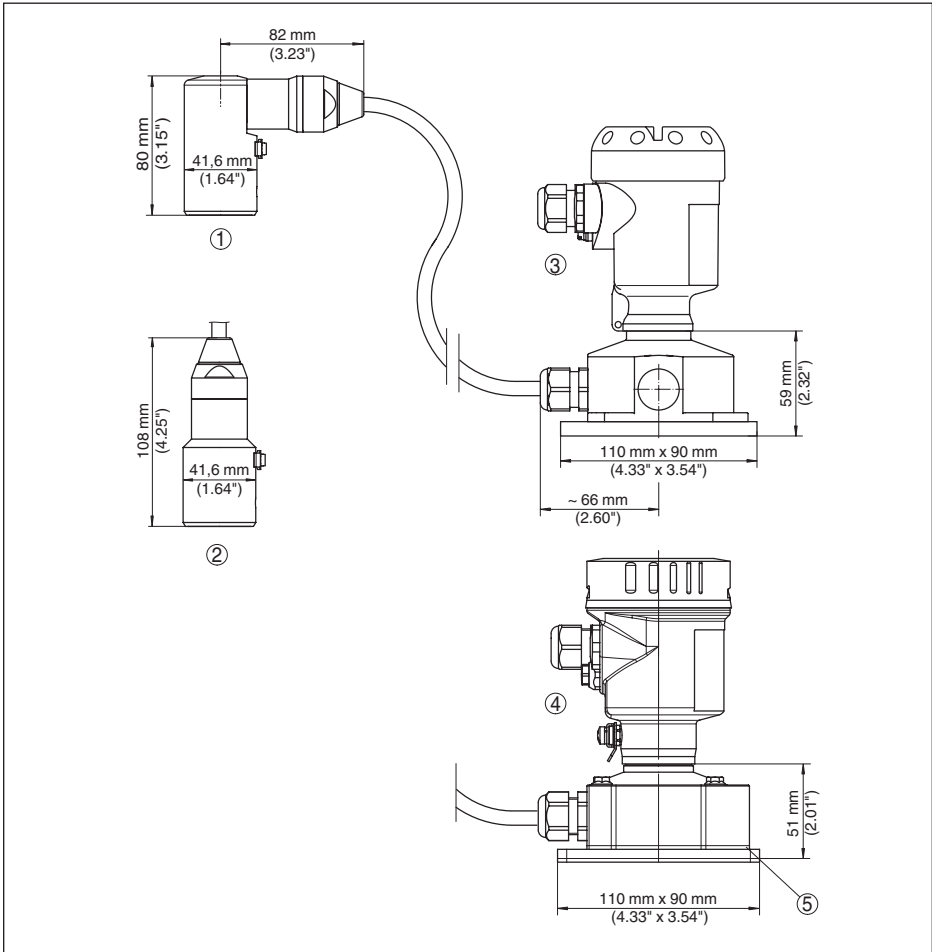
IP 68-Ausführung mit externem Gehäuse
